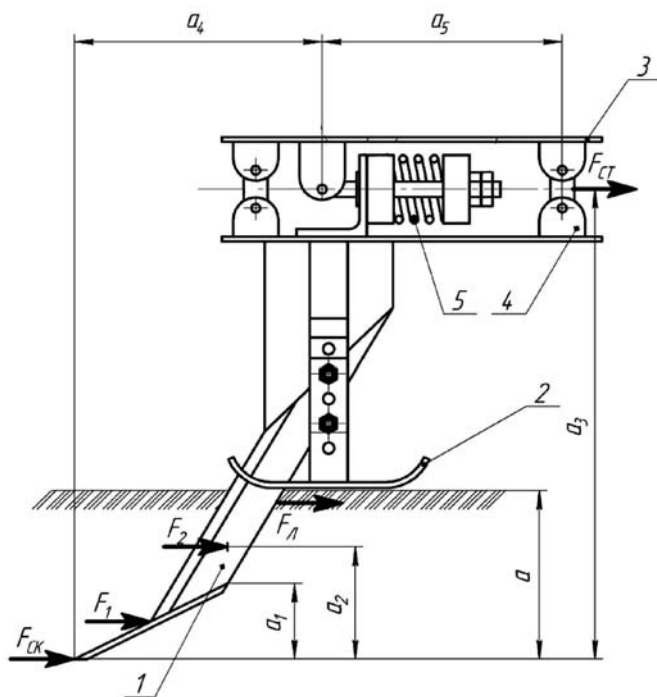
Розрахункова схема діючих сил: 1 – корпус; 2 – лижа; 3 – плита верхня; 4 – паралелограмний механізм; 5 – пружний елемент;
